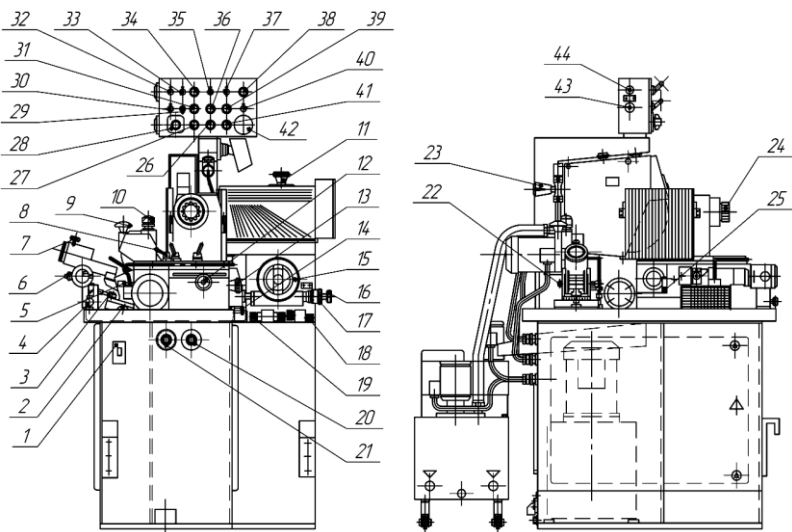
Органы управления и настройки полуавтомата для заточки сверл модели ЗЕ653
